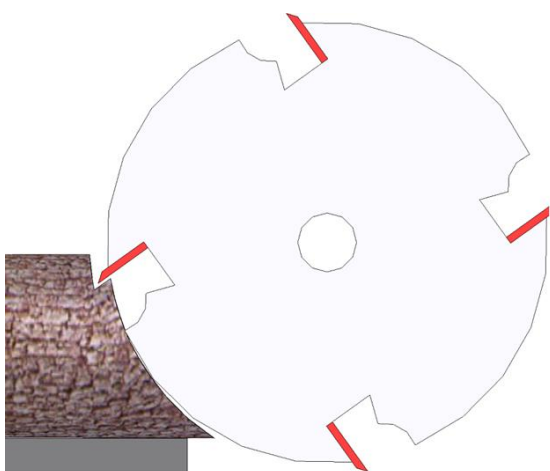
Princip funkce frézovacího mechanismu s přitlačnou deskou [5]
